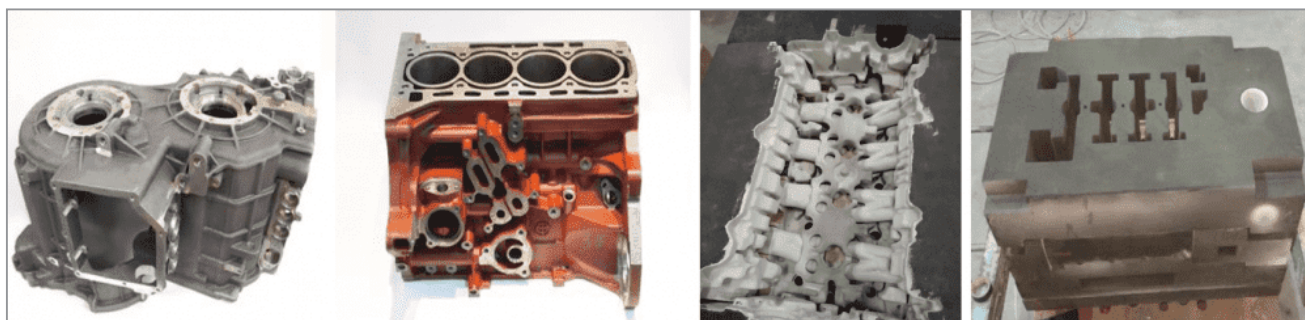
Блок цилиндров двигателя, изготовленный на оборудовании FHZL по технологии PCM
